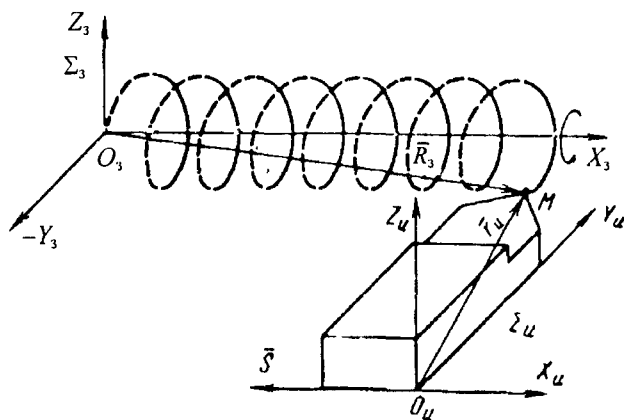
Схема движения вершины резца в координатной системе заготовки Σ_3
